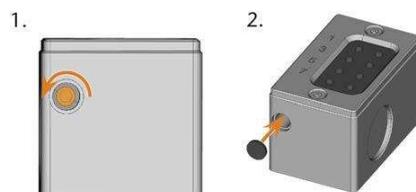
SCHRAUBE IN URSPRUNGSZUSTAND BRINGEN (LINKS) UND DIE SCHUTZKAPPE PLATZIEREN
